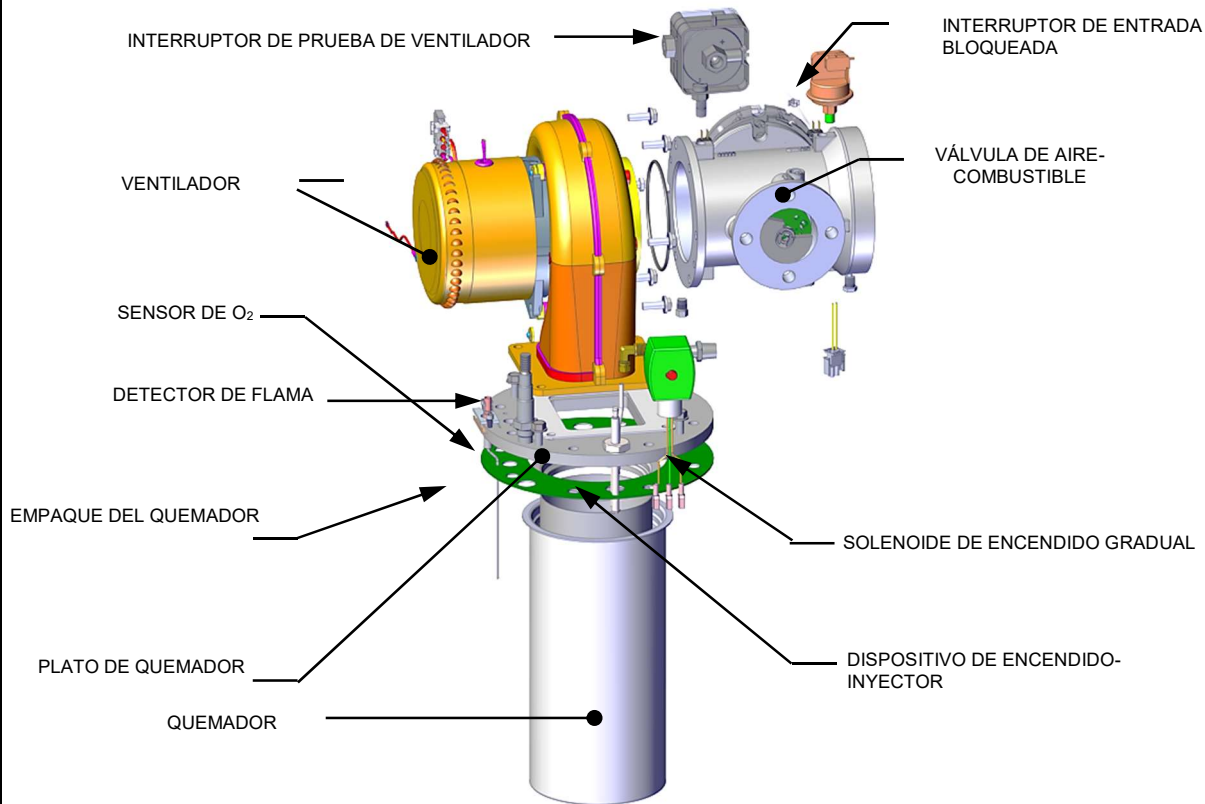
Ensamblado del quemador de BMK 750/1000 (vista detallada)
